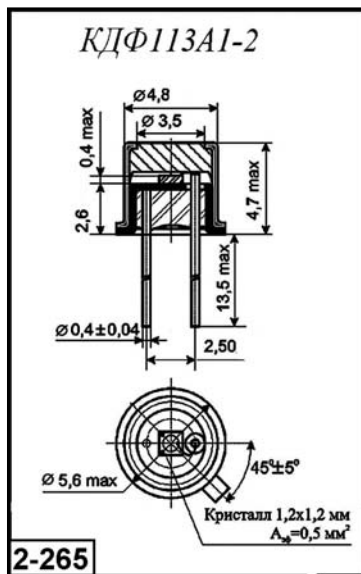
Внешний вид, габаритные размеры кремниевых фотодиодов
